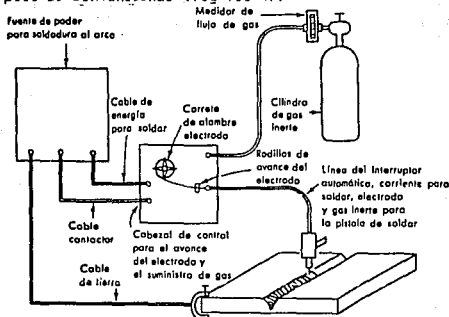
Equipo completo de la soldadura "MIG".
